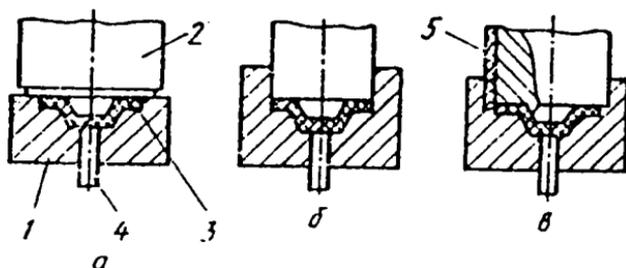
Схема пресс-форм прямого прессования: а — открытая пресс-форма; б — закрытая; в — полужакрытая: 1 — матрица; 2 — пуансон; 3 — изделие; 4 — избыточный материал; 5 — зазор между пуансоном и матрицей
